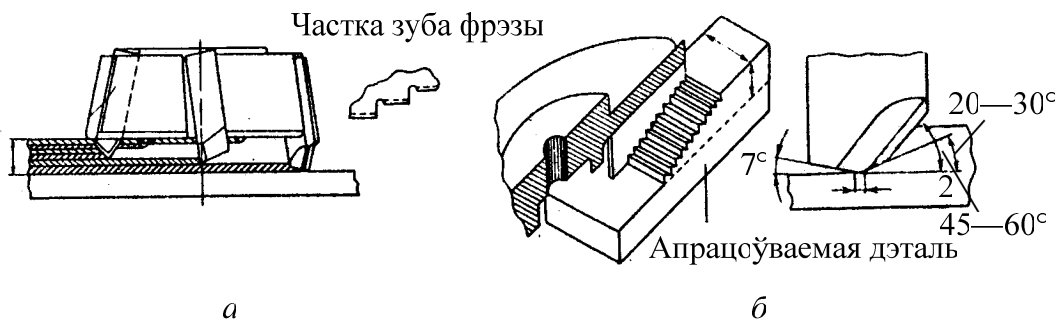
Фрезерная галоўка з паваротнымі цвёрдасплаўнымі пласцінкамі
